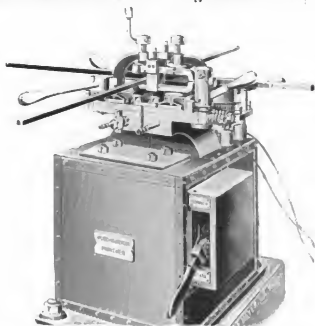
und 3. Elektrische Universal-Schweissmaschine.
